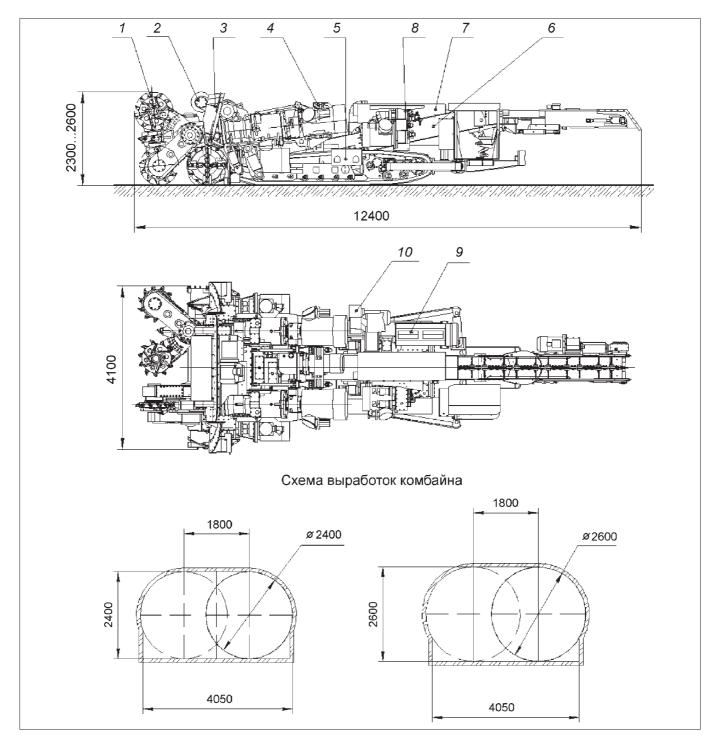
Конструктивная схема комбайна "Урал-10А": I — орган исполнительный; 2 — устройство отбойное; 3 — щит; 4 — установка бурильная; 5 — гусеничный ход; 6 — грузчик; 7 — гидросистема; 8 — насосная станция; 9 — электрооборудование; 10 — система пылезащиты
